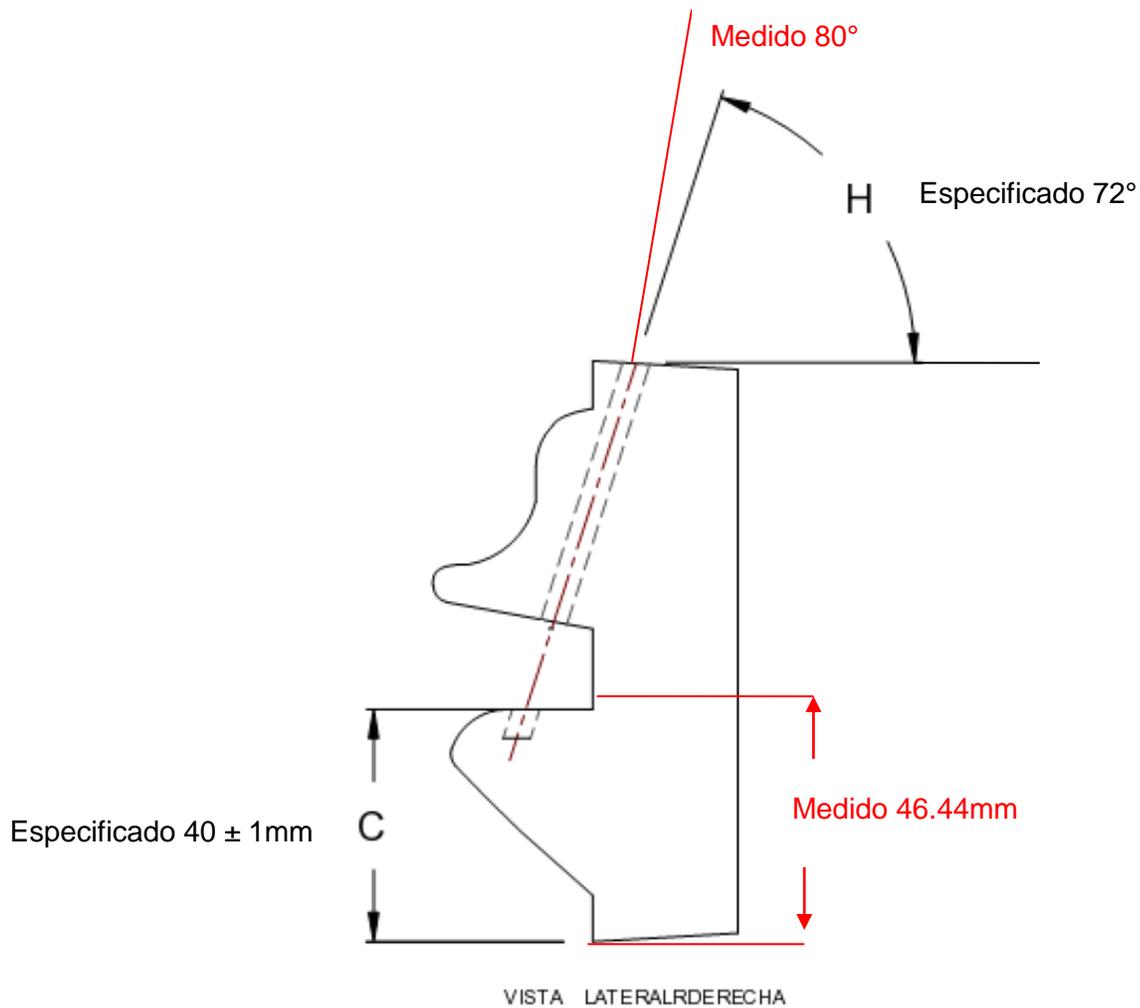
REVISIÓN DIMENSIONAL DE PLANTILLA
